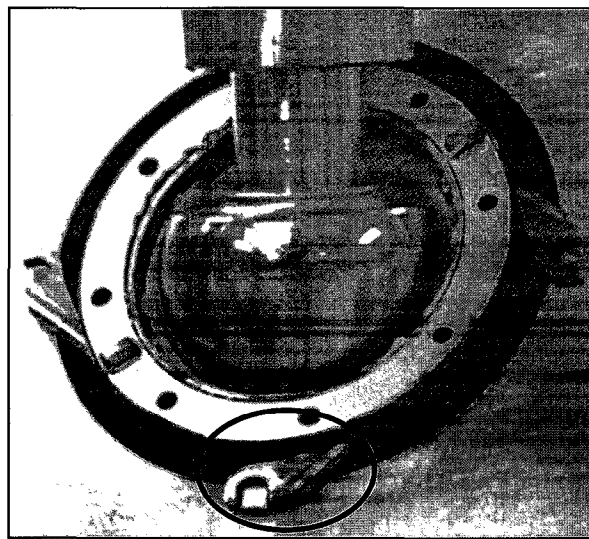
Cisaillement de la lamelle 2 lors de l'essai de rupture.
